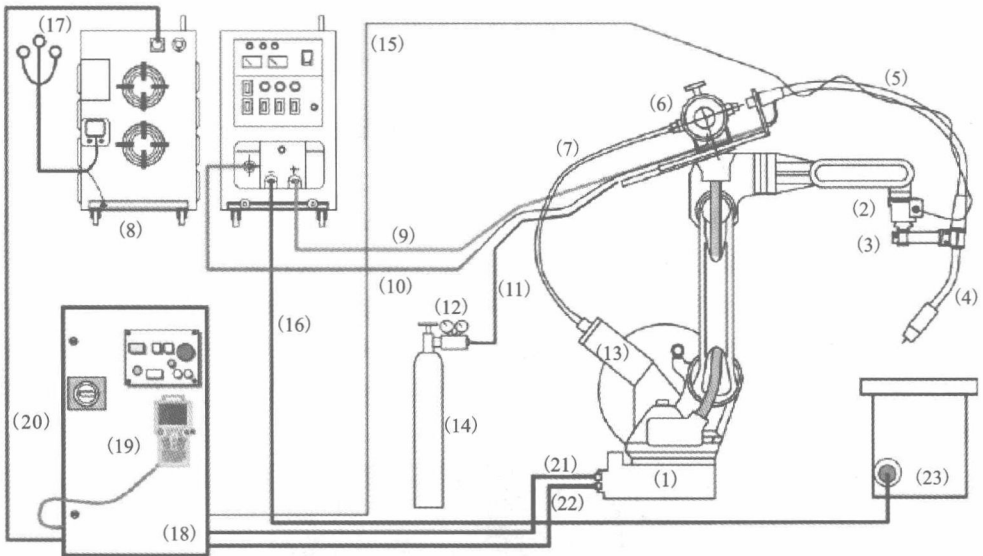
工业机器人气体保护焊工作站基本构成
